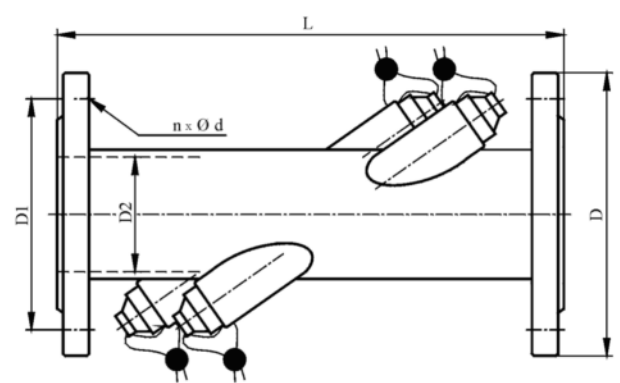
Габаритные и установочные размеры датчиков потока 2 класса точности
